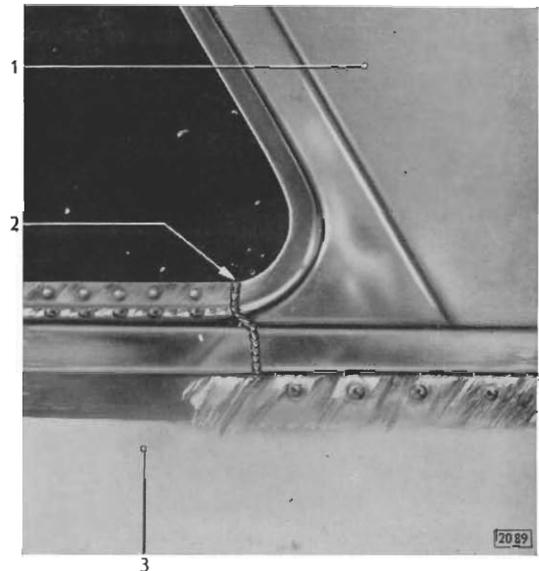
Stoßfuge zwischen Seitenwand und Rückwandscheibensäule autogen zugeschweißt
